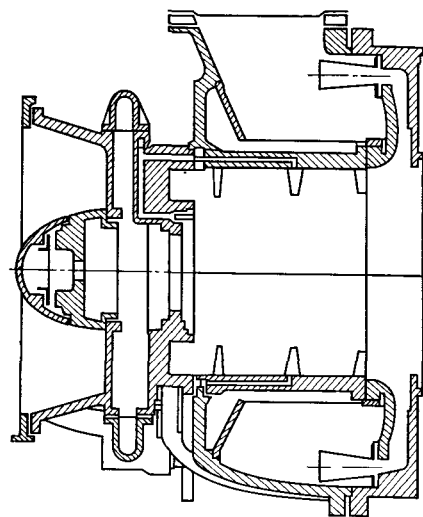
Двухстенный корпус компрессора ГТУ ЕМ-27Р с разъемным внутренним и неразъемным внешним корпусом фирмы Инглиш Электрик
